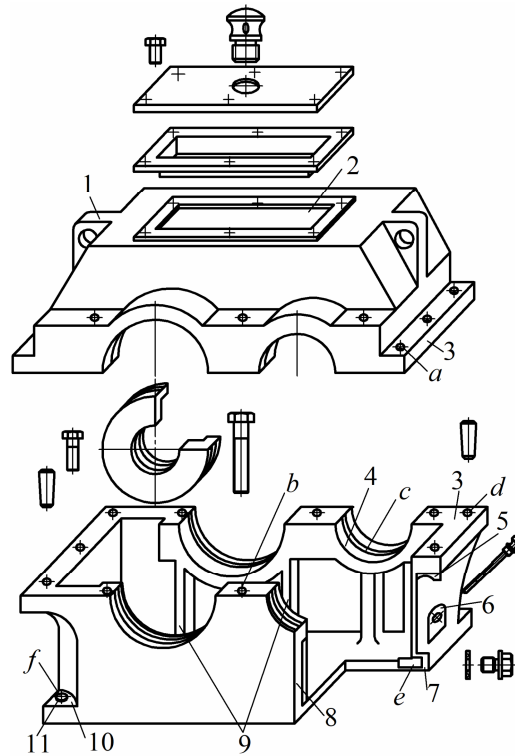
Детали корпуса цилиндрического одноступенчатого редуктора
